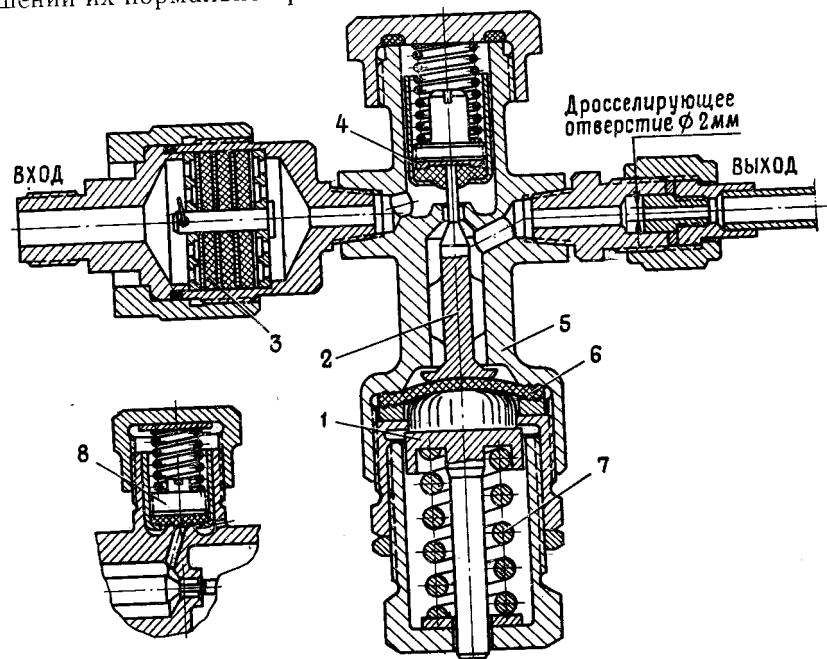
Воздушный редуктор ИЛ611-150-70:
